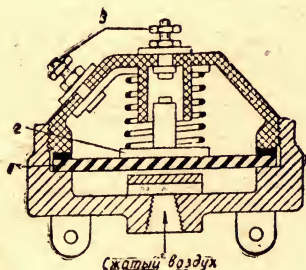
Включатель стоп-сигнала, устанавливаемый на автомобилях с пневматическим приводом тормозов
